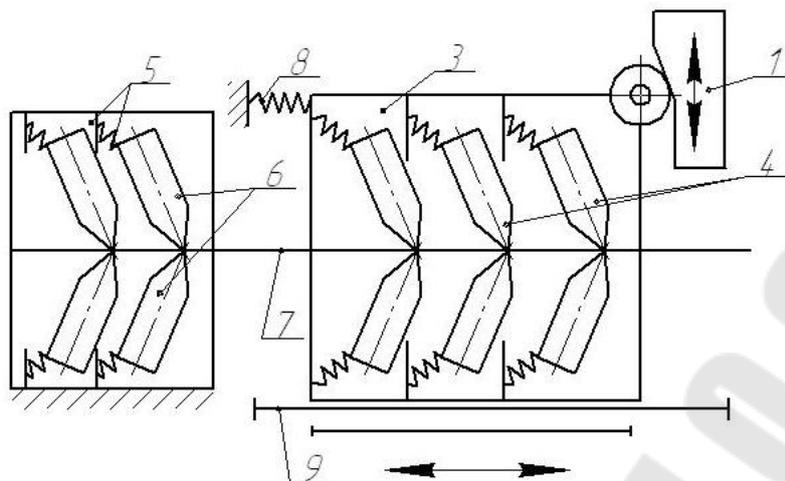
Схема ножевой подачи с приводом от ползуна прессы 1- клин, 2-ролик, 3-подвижная каретка, 4-ножи подвижной каретки, 5- неподв-я каретка, 6 - ножи неподвижной каретки, 7-лента, 8-пружины, 9-направляющие
